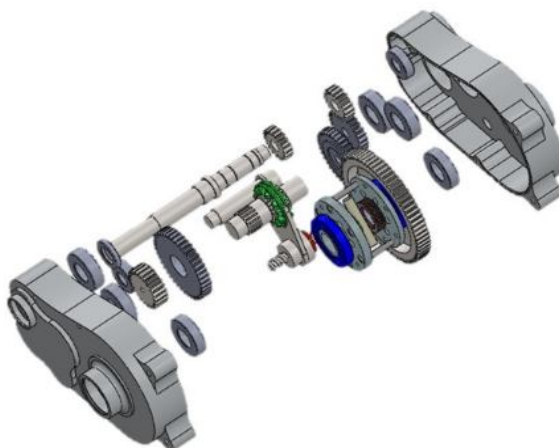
Коробка перемины швидкостей в SolidWorks.
